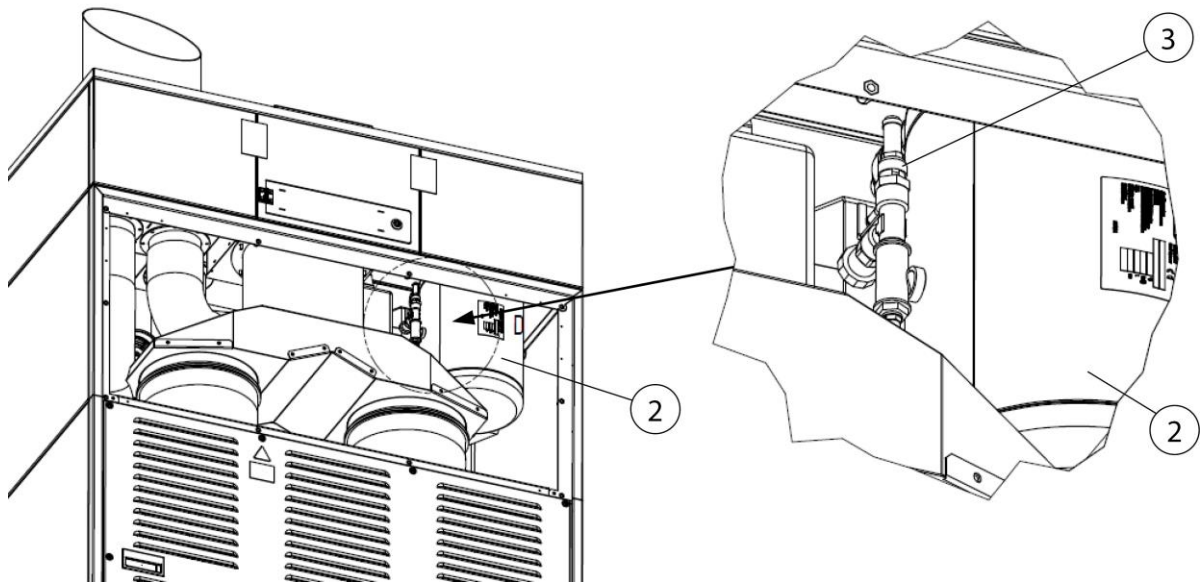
Accès à la soupape de sûreté pour air comprimé
